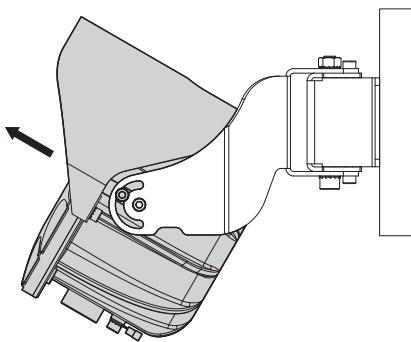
Монтаж на стену (вертикальное перемещение, +30°).
